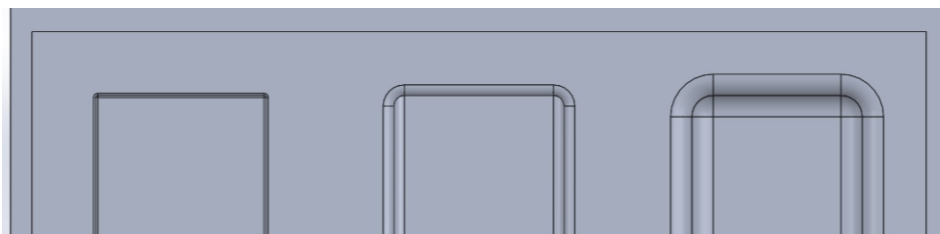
Desenho CAD molde com razão de estiramento de 1,67 – 2
